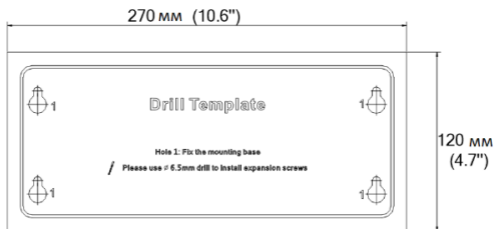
Шаблон крепления (монтажная коробка)
